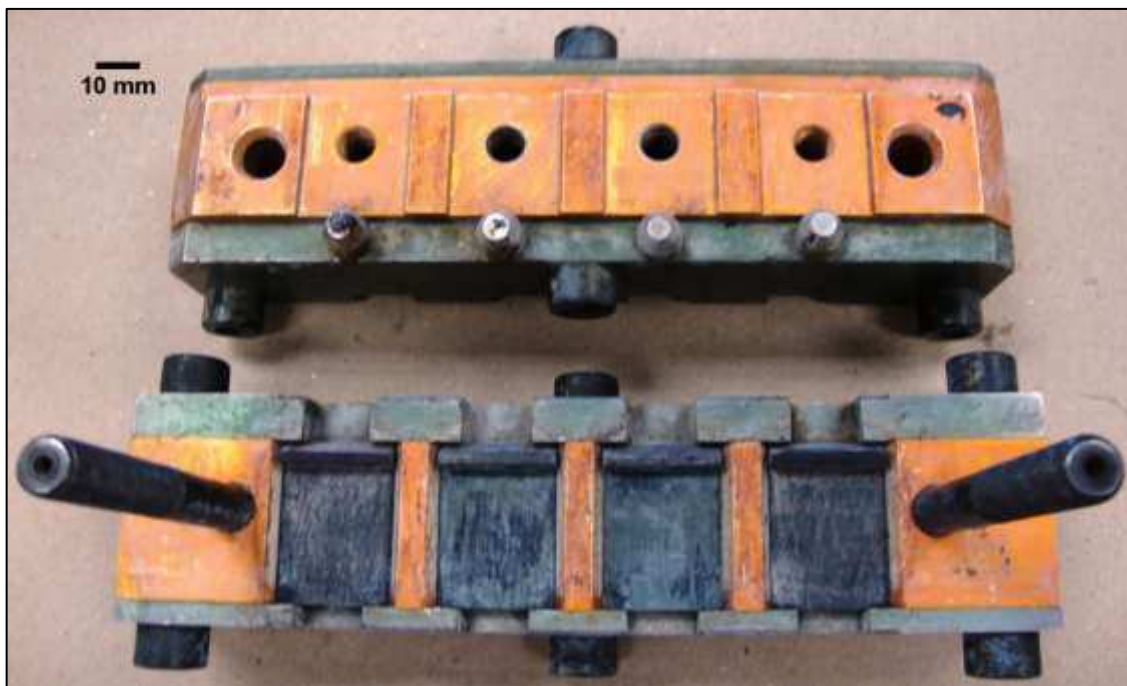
Dispositivo de colagem (Fonte: Autor)
